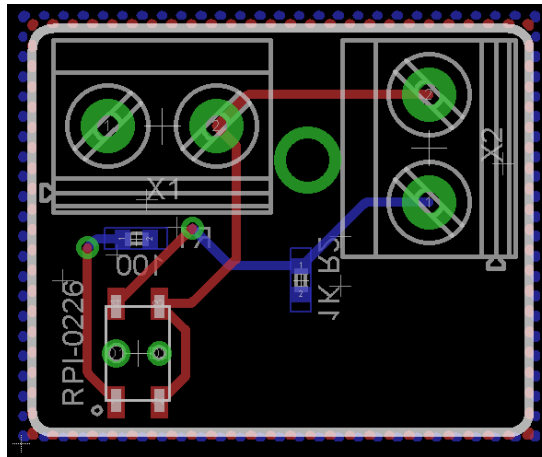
Esquema em EAGLE da PCB para o interruptor ótico RPI-0226
